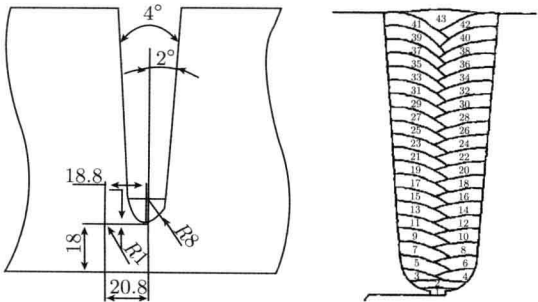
焊道结构和顺序 (单位: mm)
